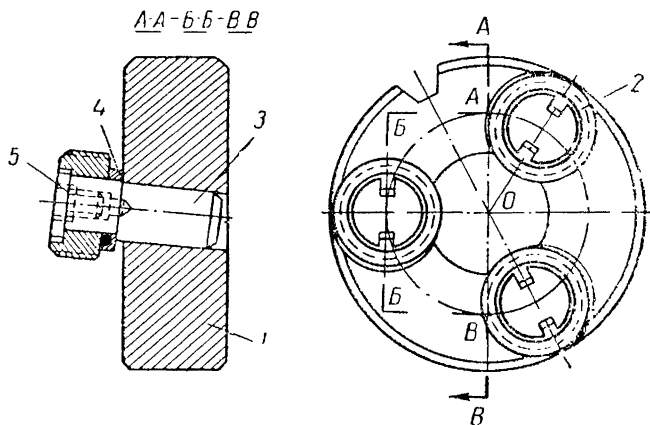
Нераскрывающаяся резьбонакатная головка.
